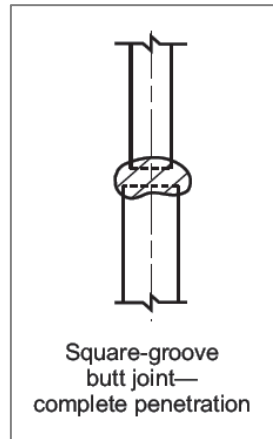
Soldaduras en junta vertical a tope [18]
